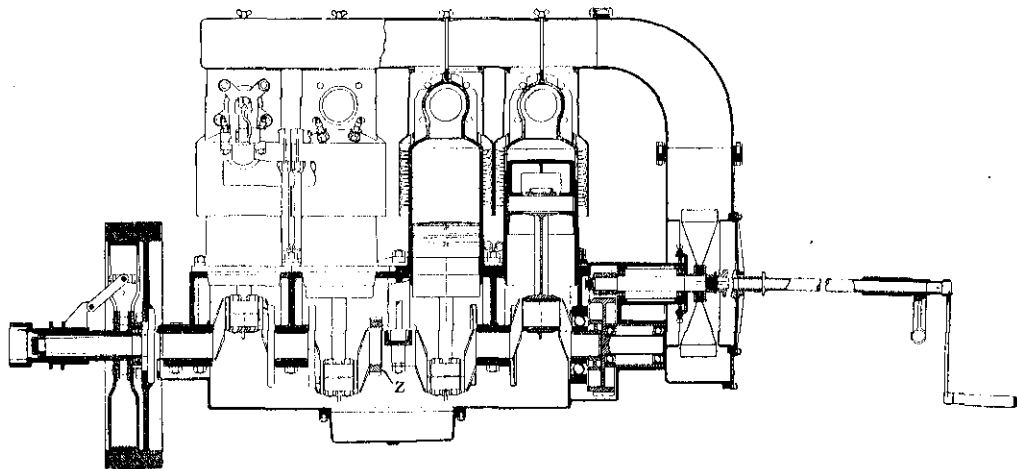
Охлаждающійся воздухомъ двигатель Фрайеръ-Миллера.
